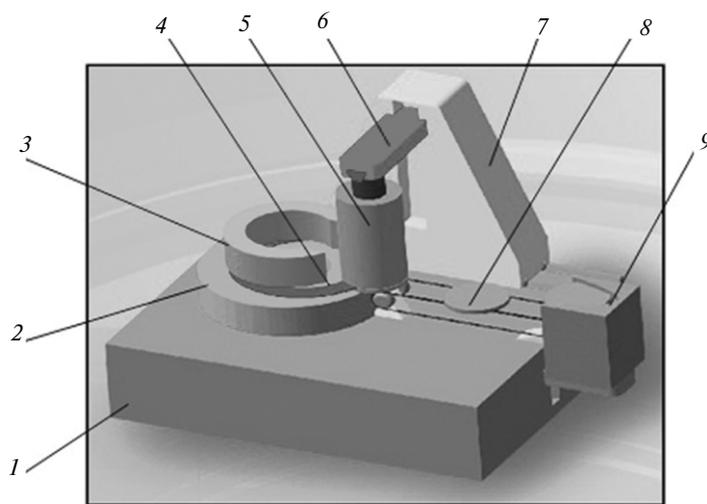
Компьютерная модель станка резки слитка кремния на пластины алмазным отрезным кругом с внутренней режущей кромкой напроход: 1 — стол; 2 — нижний индуктор; 3 — верхний магнитопровод; 4 — ротор-инструмент; 5 — разрезаемый монокристалл; 6 — кронштейн механизма продольной подачи; 7 — механизм поперечной подачи; 8 — отрезанная пластина; 9 — касетировщик.
